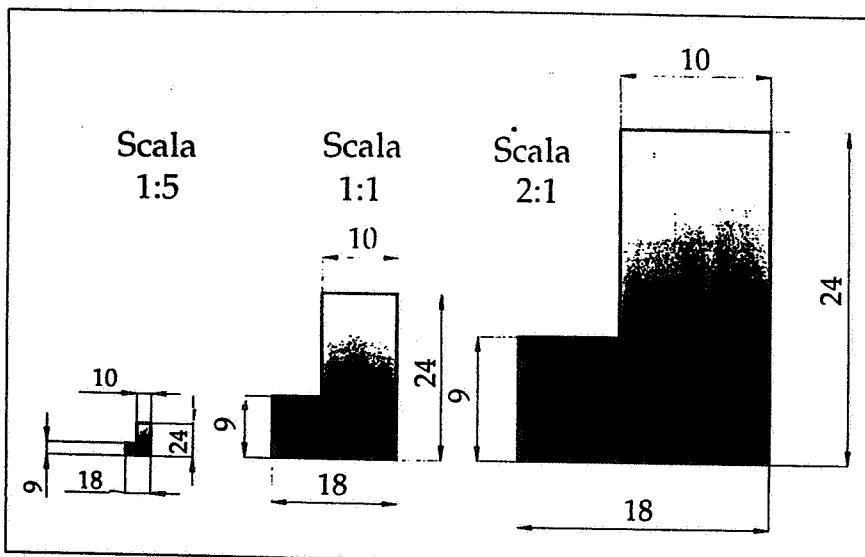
Rappresentazione dello stesso oggetto secondo diverse scale.
